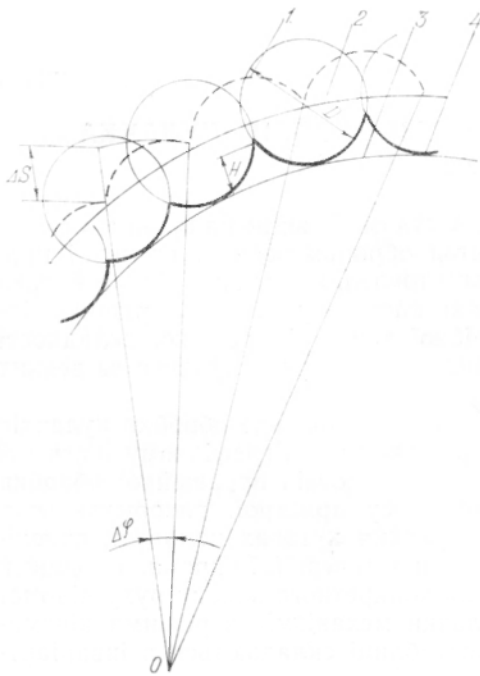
Робочий участок поверхні кулачка. 1 — траектория движения центра ролика; 2 — эквидистанта кулачка; 3 — теоретический профиль; 4 — реальный профиль кулачка.
